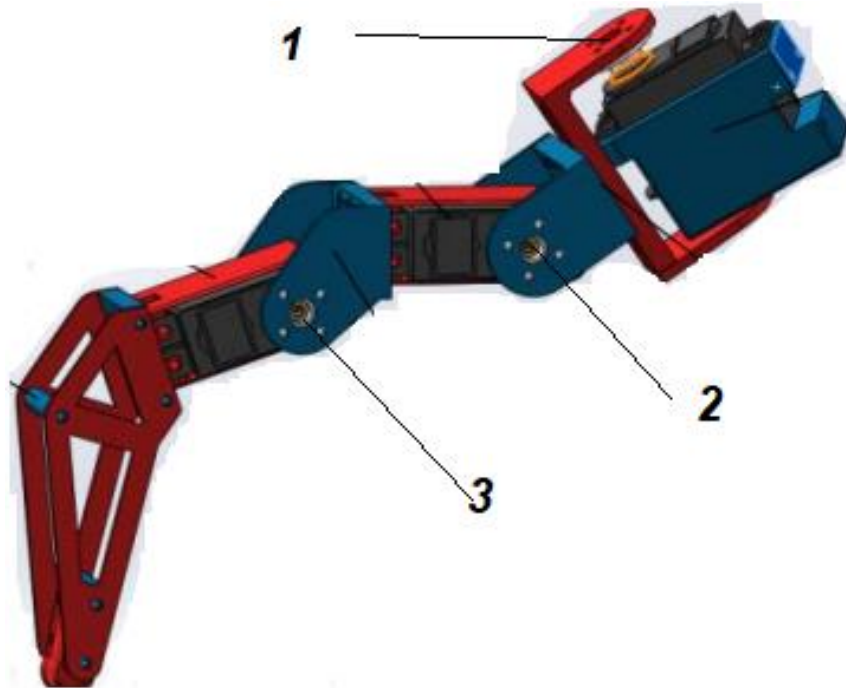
Загальний вигляд ноги МРГ – опора мехатронної конструкції
